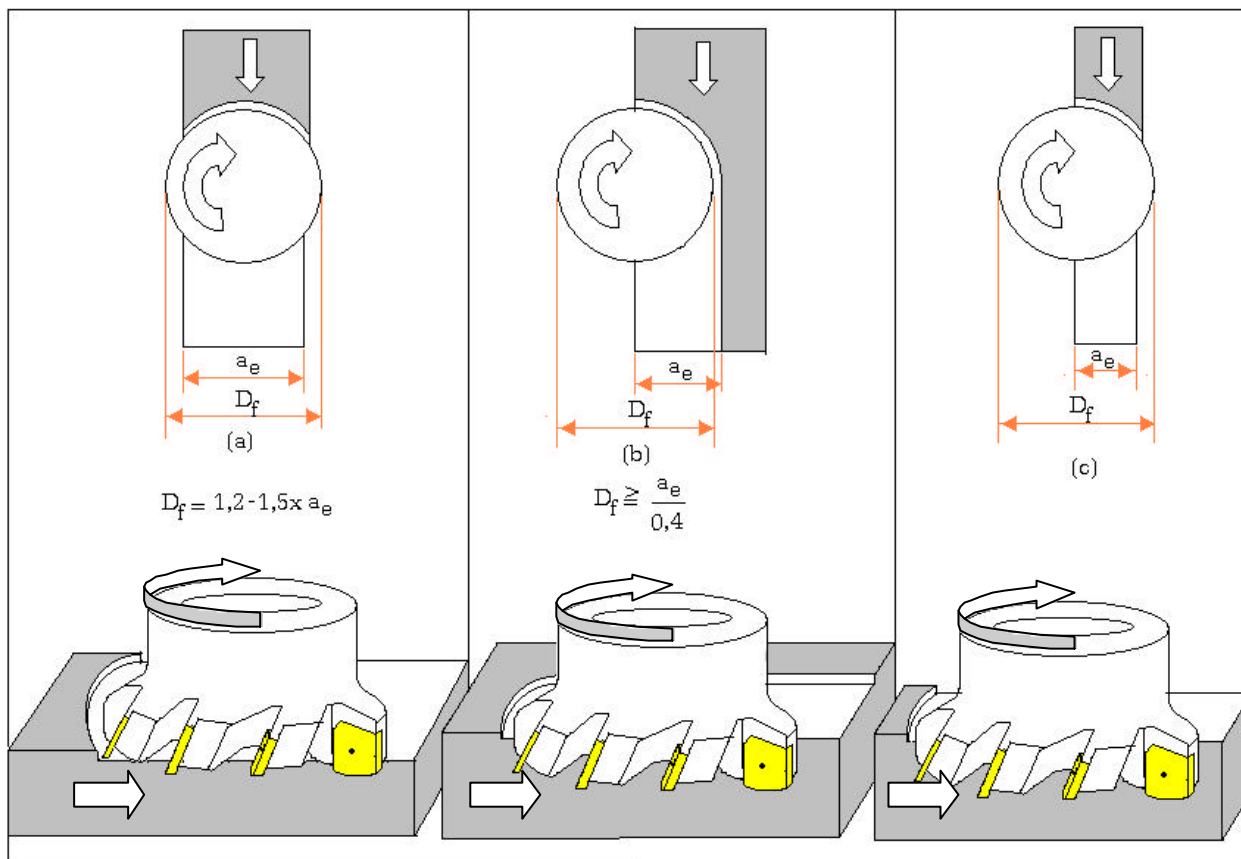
Posições da fresa em relação à peça no fresamento frontal
